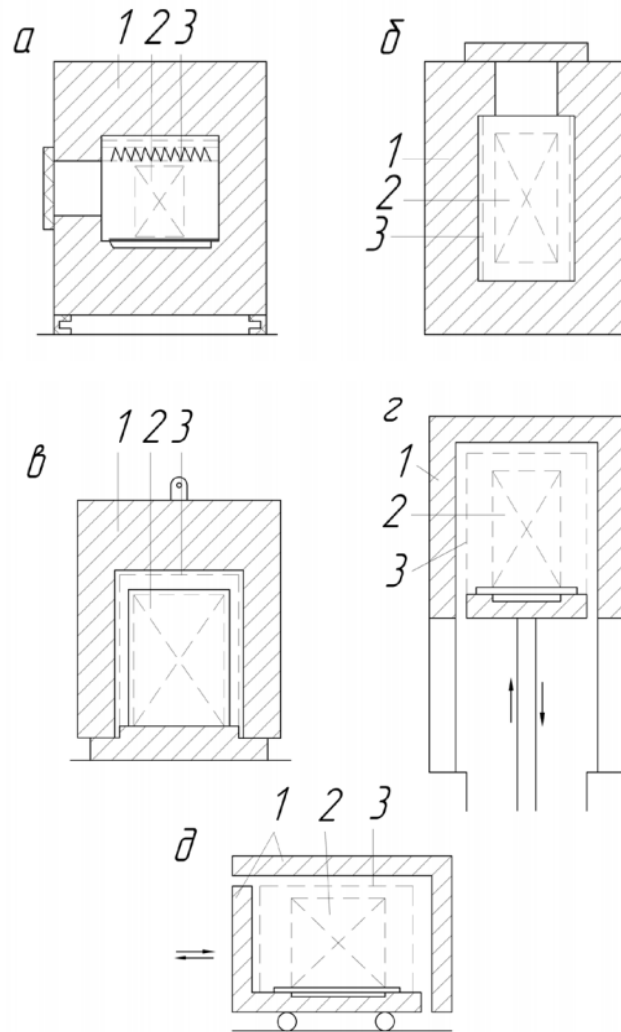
Основні типи печей опору періодичної дії: а - камерна; б - шахтна; в - ковпакова; г - елеваторна; д - з висувним подом; 1 - кладка печі, 2 - садок, 3 - нагрівачі
